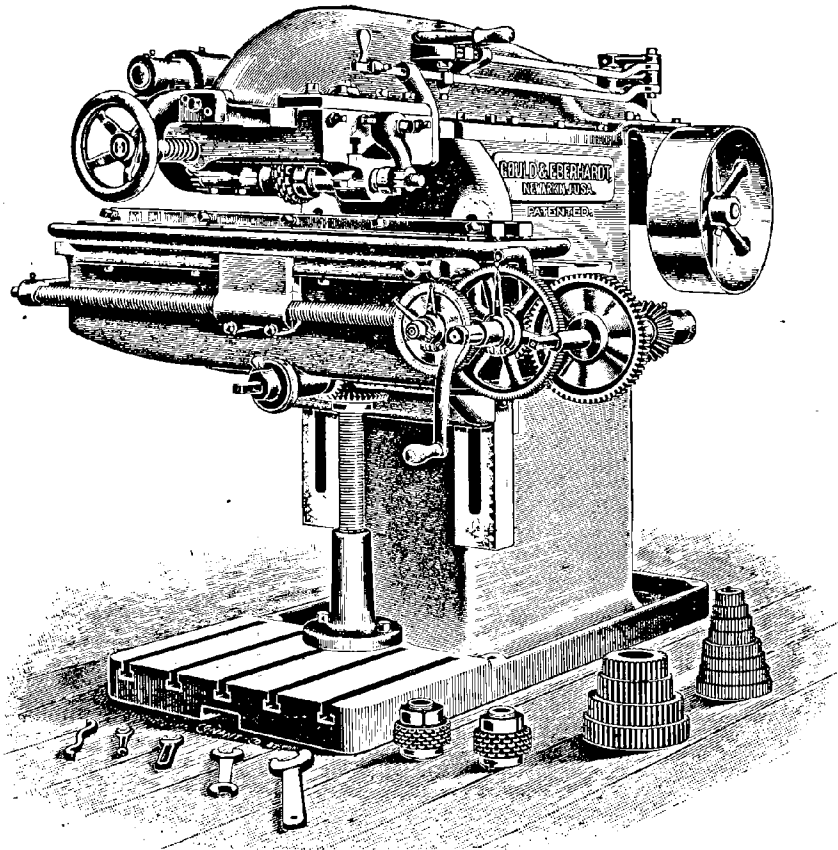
Machine demi-automatique spéciale pour le taillage des crémaillères.
